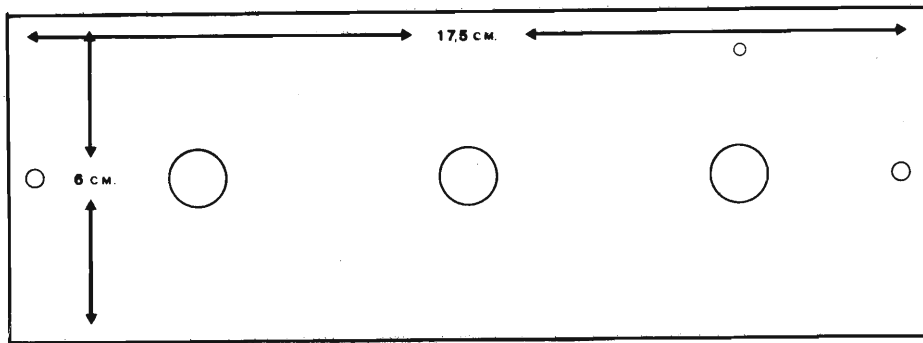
Piano di foratura e dimensioni del pannello anteriore.
